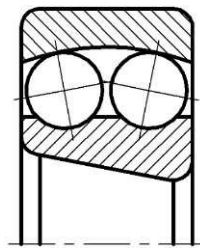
Дворядний сферичний кульковий підшипник
